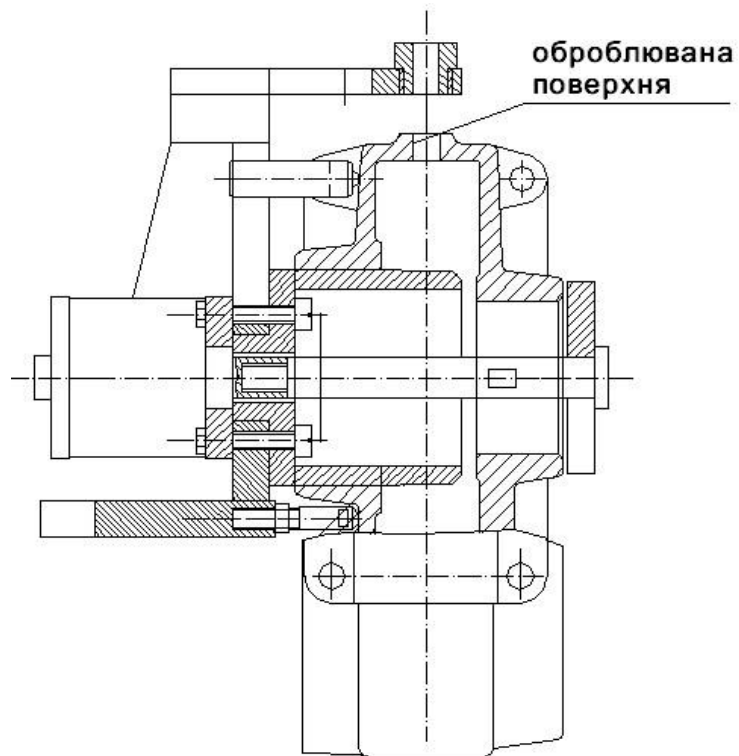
Схеми пристосувань для обробки корпусу (продовження)
